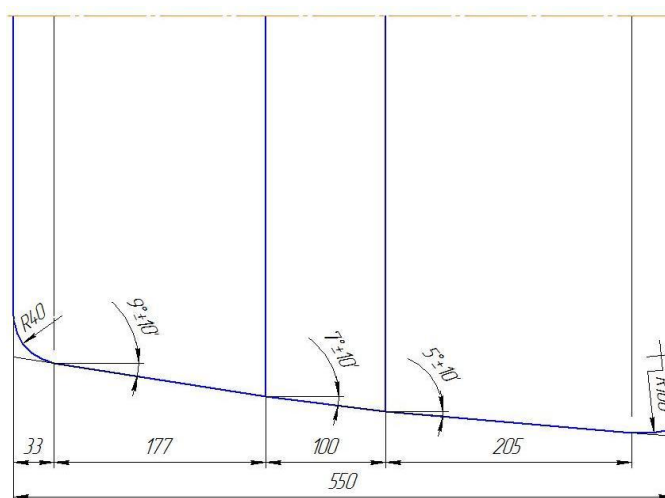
Калибровка валка трехвалкового обкатного стана для ведения процесса обкатки с уменьшением диаметра черновой трубы
